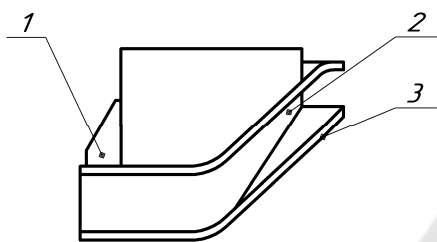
Копир: 1 – корпус; 2 – дорожка копира; 3 – ребро
